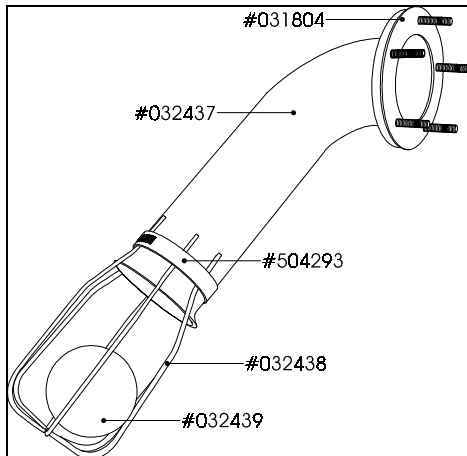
ASSEMBLAGE DU CLAPET ANTI-RETOUR
